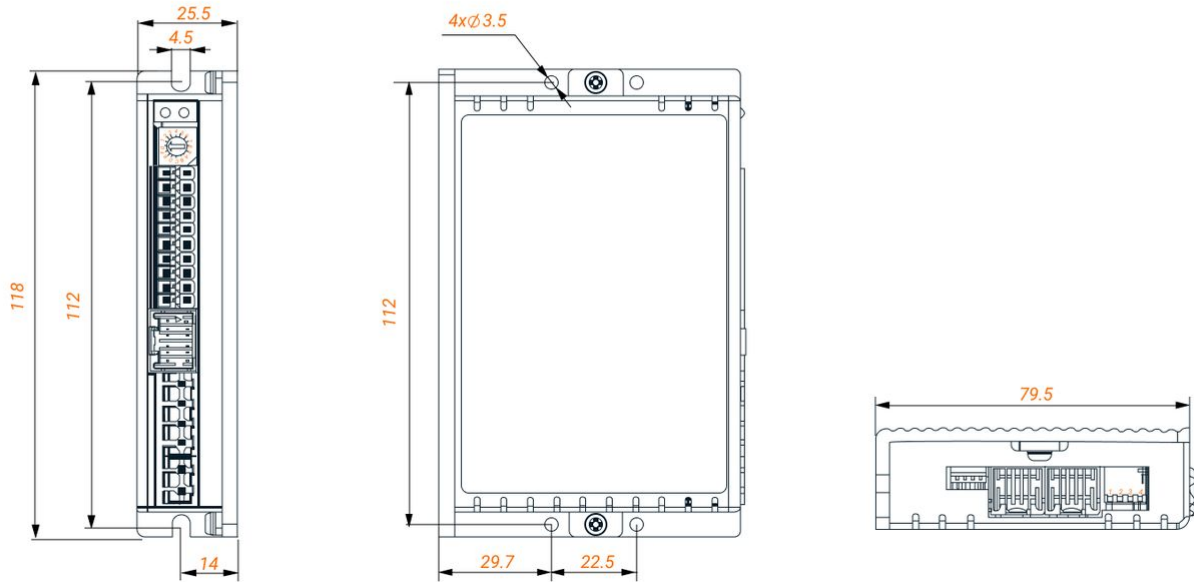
Габаритные размеры драйвера ELD2-RS7010
